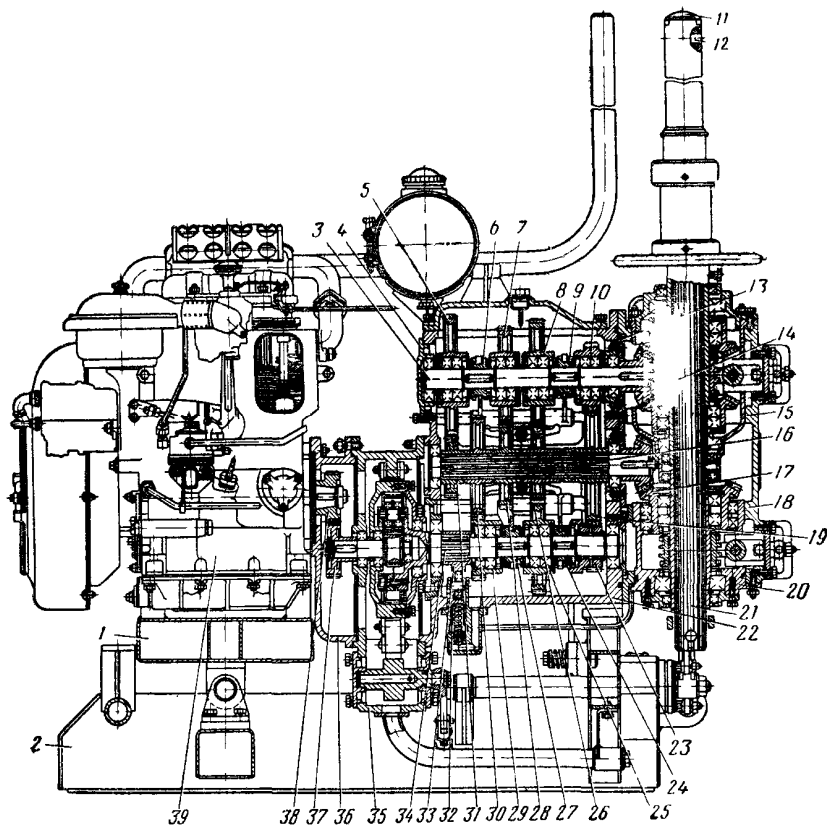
Двигатель и трансмиссия бурового агрегата:
